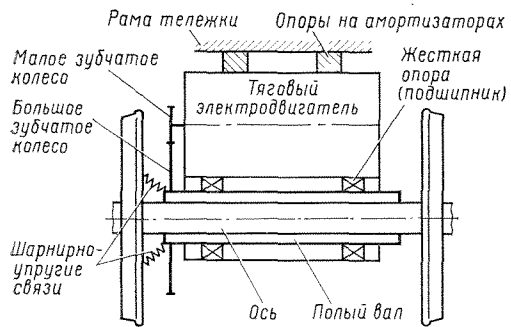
Схема опорно-рамной подвески тягового электродвигателя
